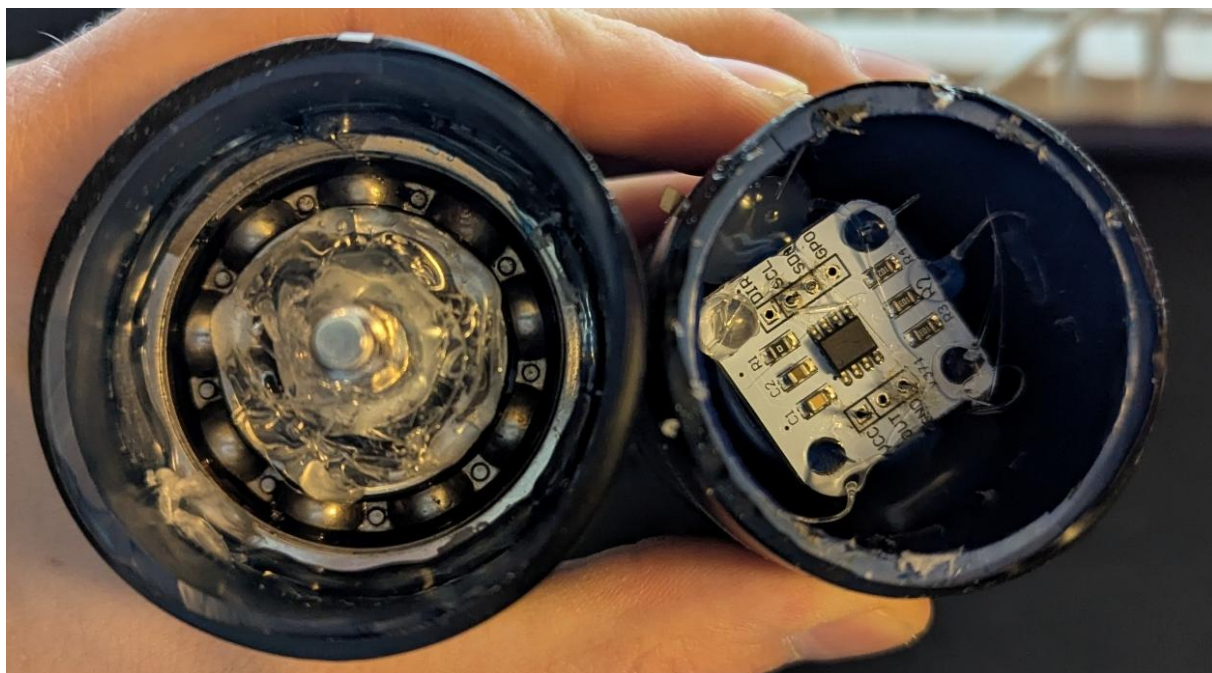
Слева крышка корпуса, справа корпус. В крышке виден стальной подшипник, на котором держится ось, магнит и болт, справа в корпусе расположена плата магнитного энкодера AS5600.
